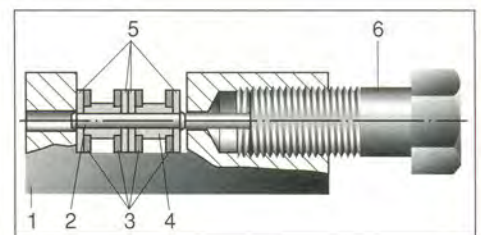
Приспособление для выпрессовки пальца цепи: 1 – скоба; 2 – палец цепи; 3 – внутренние пластины; 4 – втулка; 5 – наружные пластины; 6 – болт-выталкиватель.
